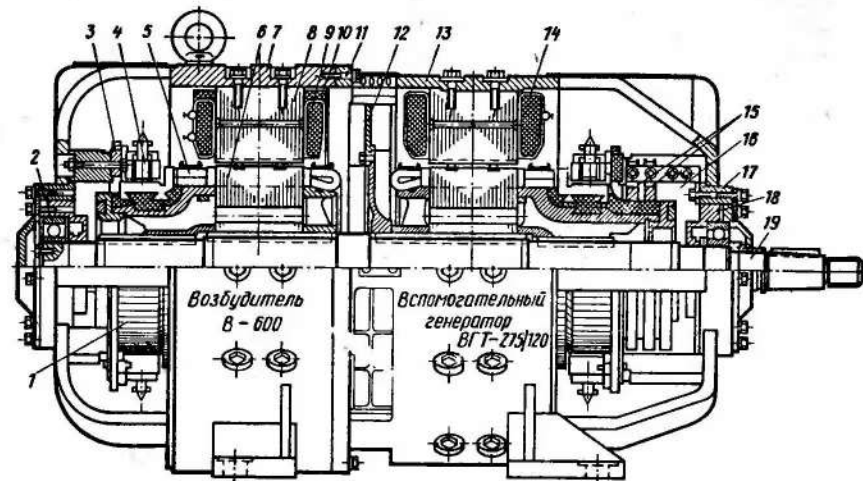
Двухмашинный агрегат типа А-706Б (продольный разрез):
